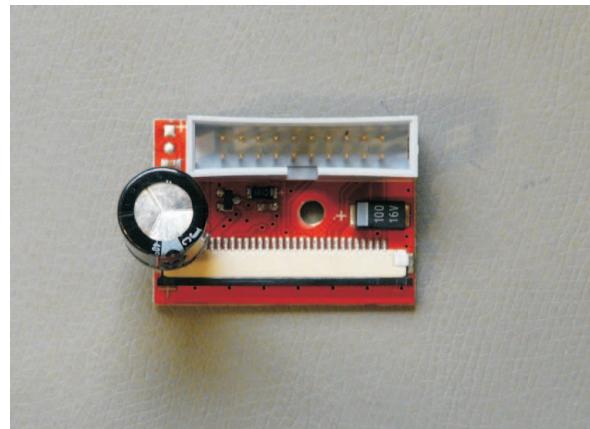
PCB – matična ploča sa SMT i Trough hole komponentama
